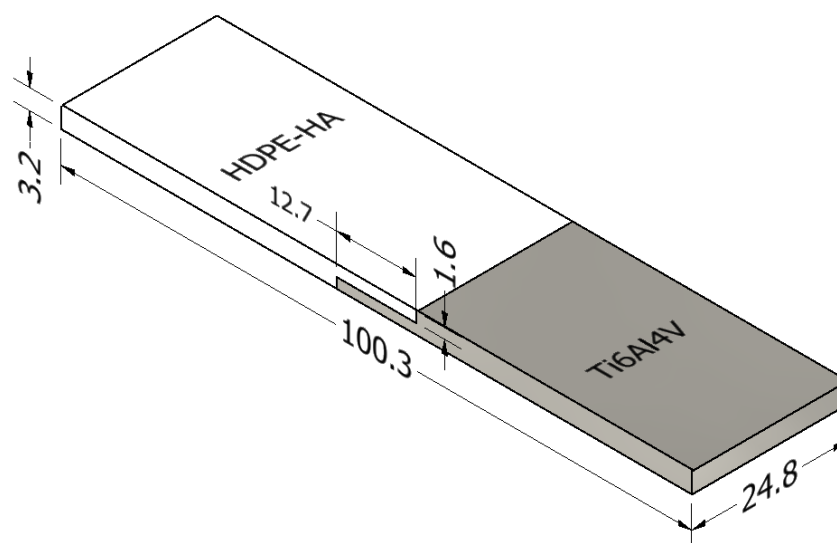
Geometria das juntas híbridas produzidas por sobremoldagem por injeção. Dimensões em mm.
